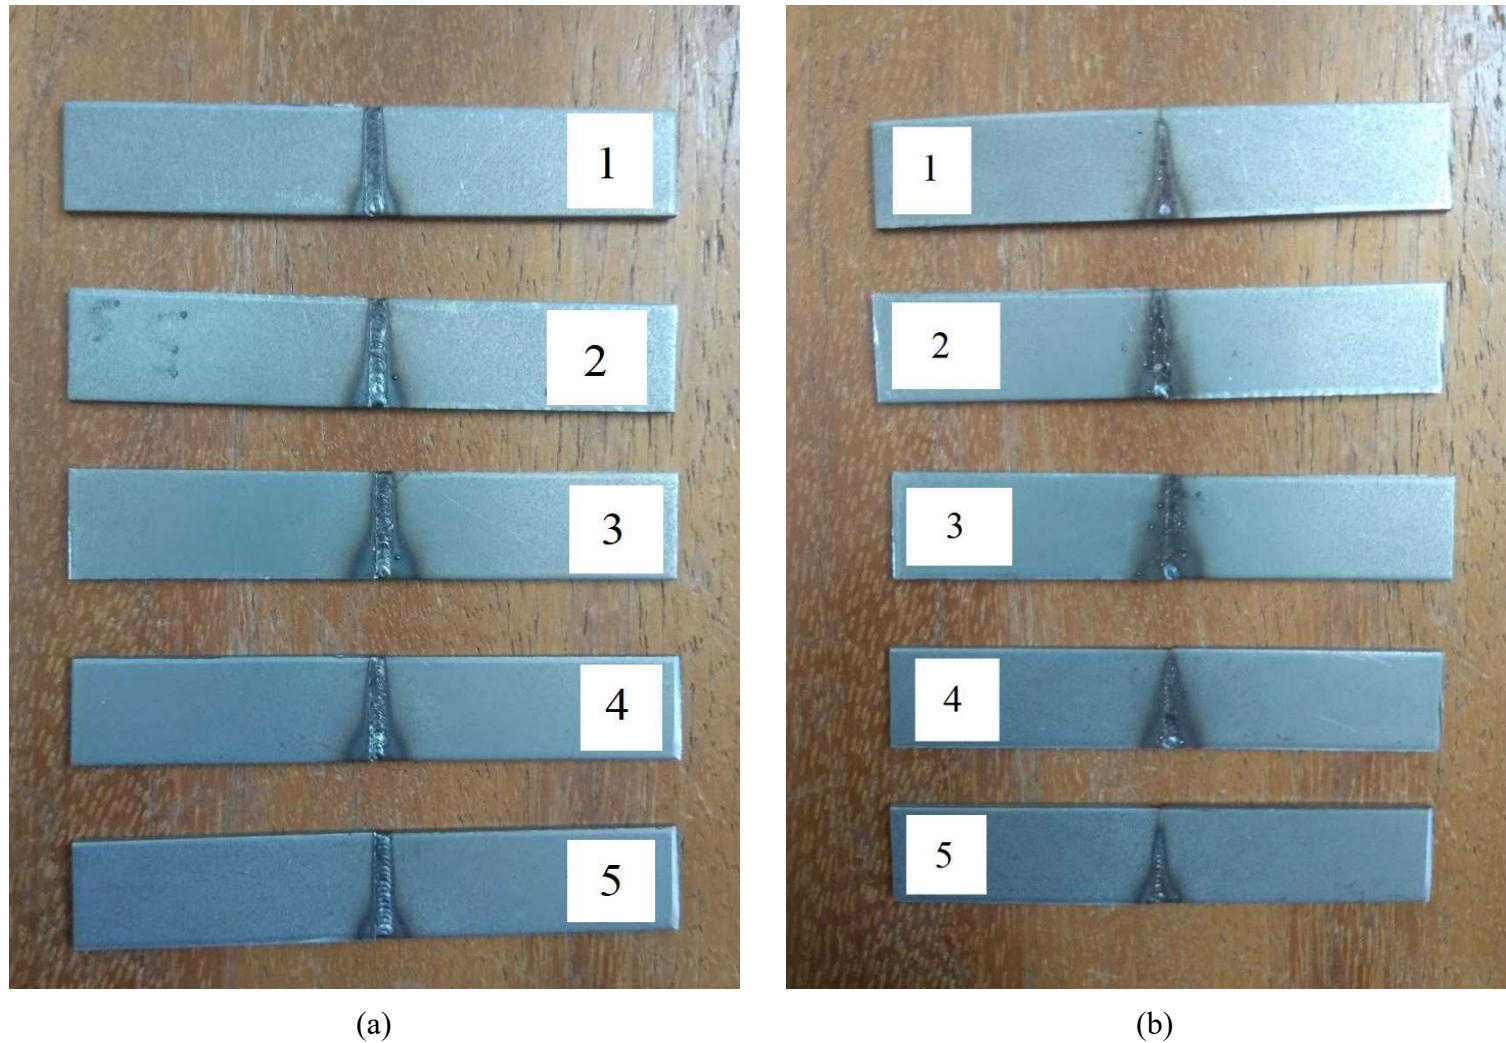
Amostras de Gen3 980T soldadas. (a) Parte superior da soldadura. (b) Raiz da soldadura
